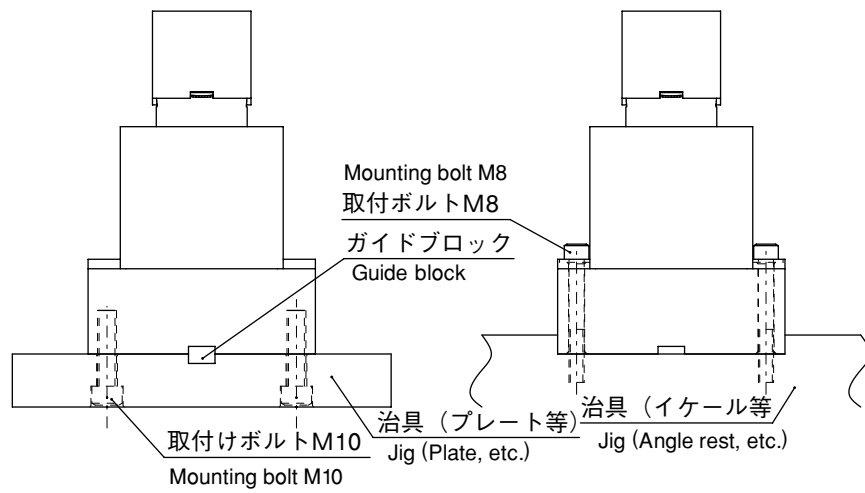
治具モジュール取付図 Jig Module Mounting
